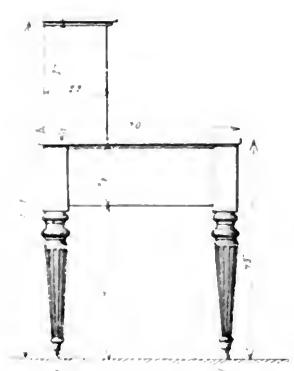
, 10 Machine à imprimer les billets de chemin de fer
